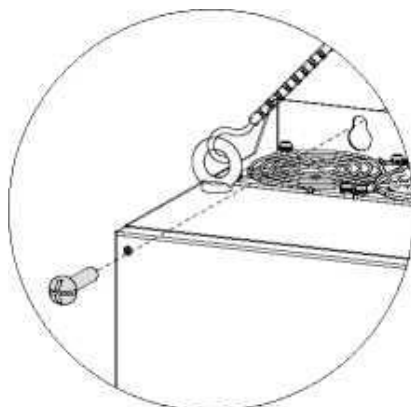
Подъем устройства INVERTER (корпус из листового металла)
